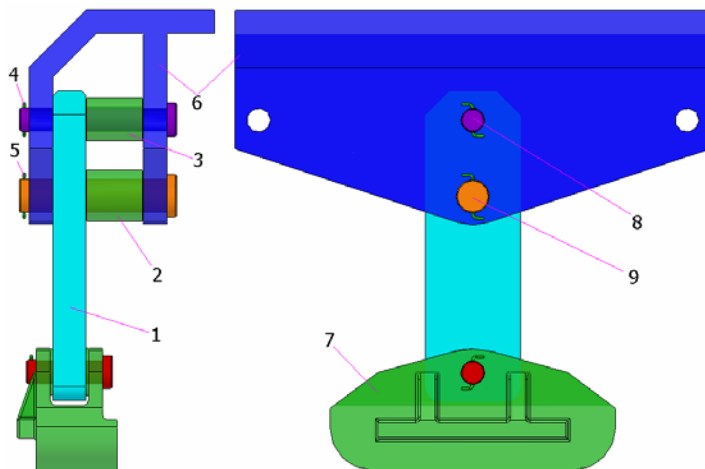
Modificările efectuate în construcția patinei dinspre front montată pe mecanismul de avans
